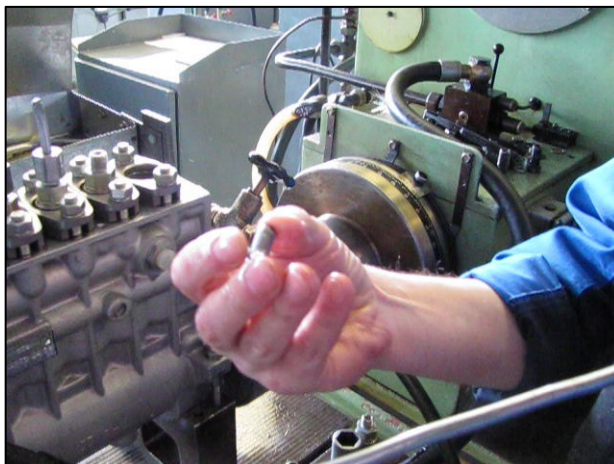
Снятие пружины, упора и нагнетательного клапана
